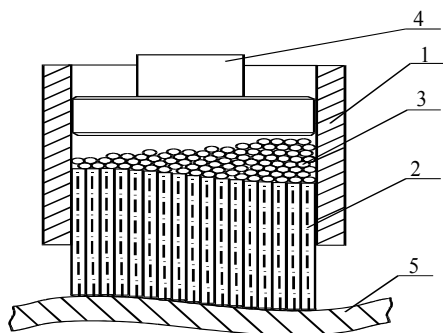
Схема многоконтактного виброударного инструмента ШСУ: 1- корпус; 2- стержни; 3- стальные шары; 4- ударник; 5- деталь
